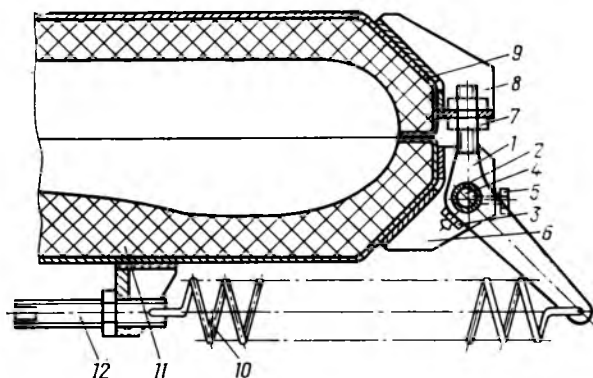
Конструкция шарнира с компенсатором массы верхней ванны
